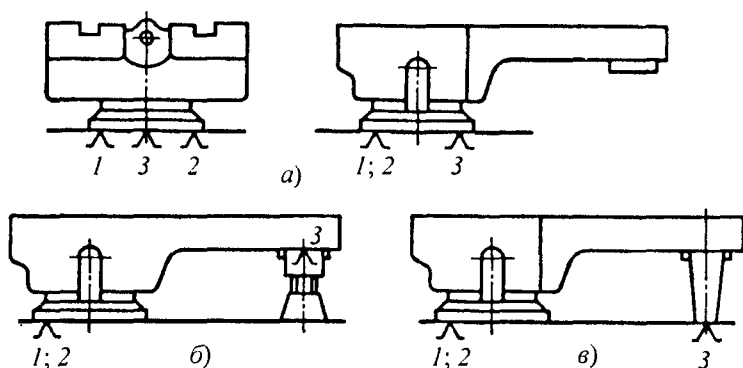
Примеры увеличения габаритных размеров установочной базы
